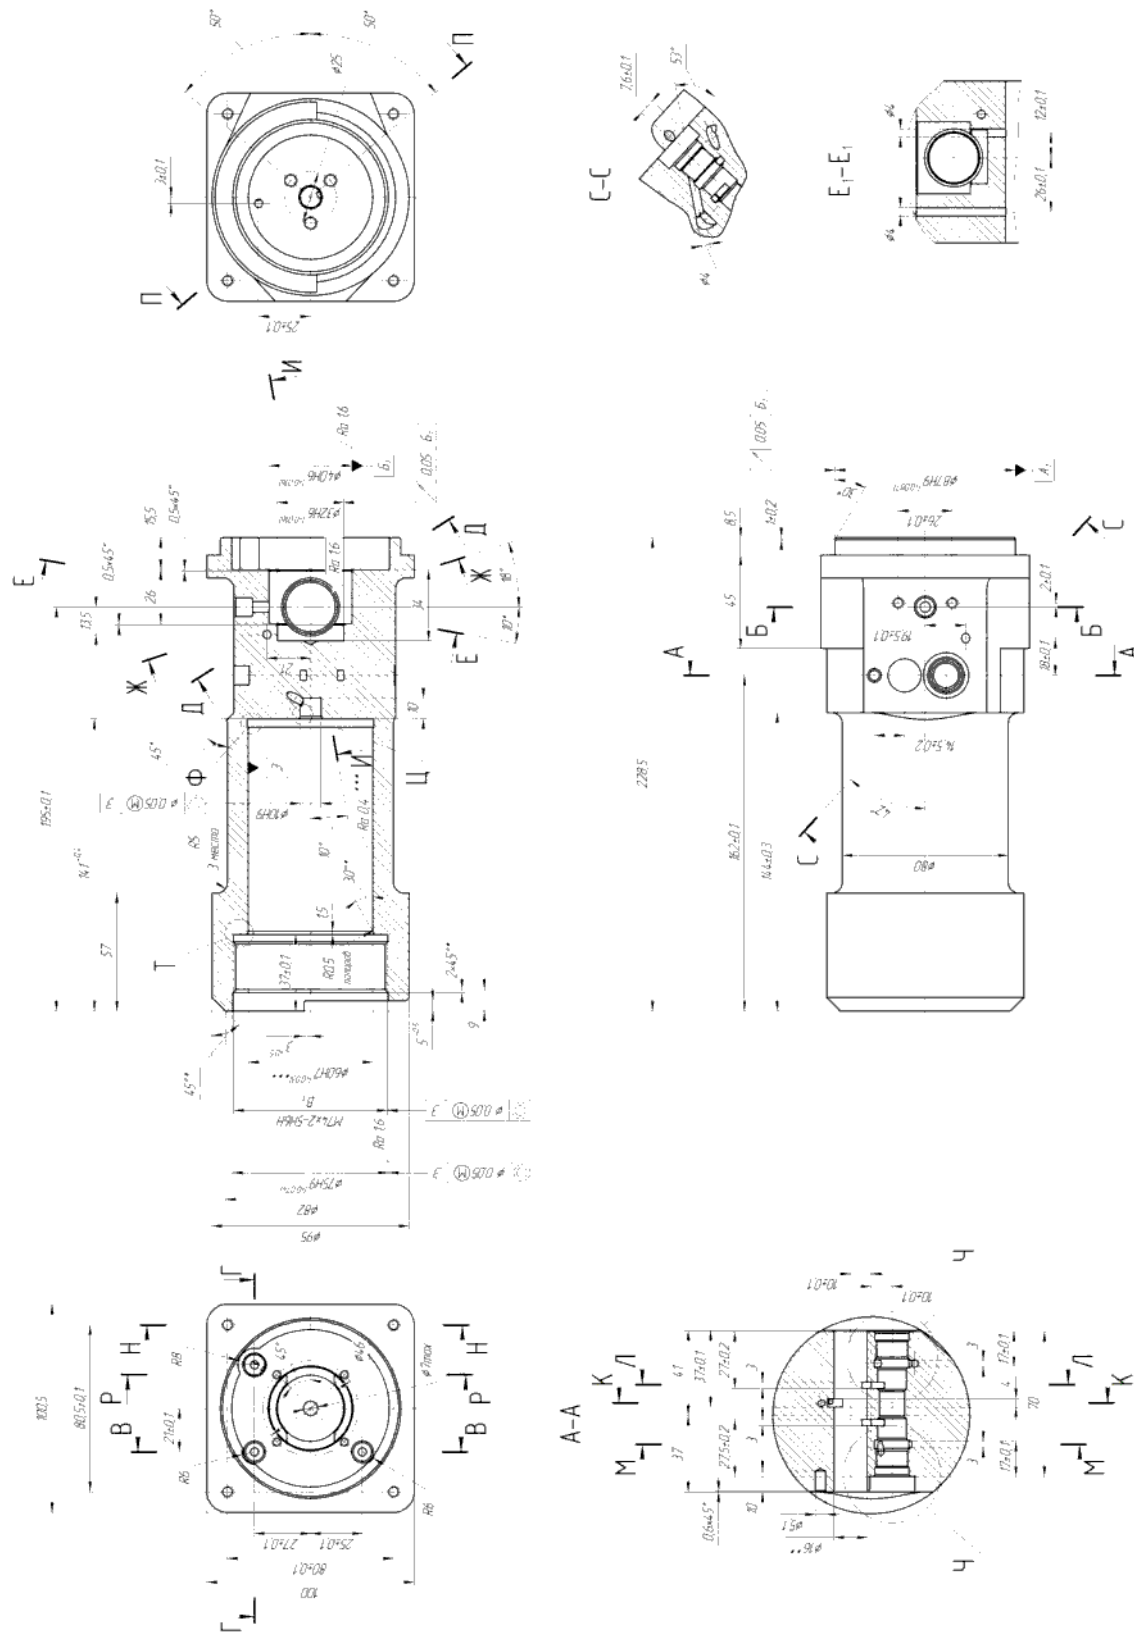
Конструкция корпуса гидроблока. Лист 1
